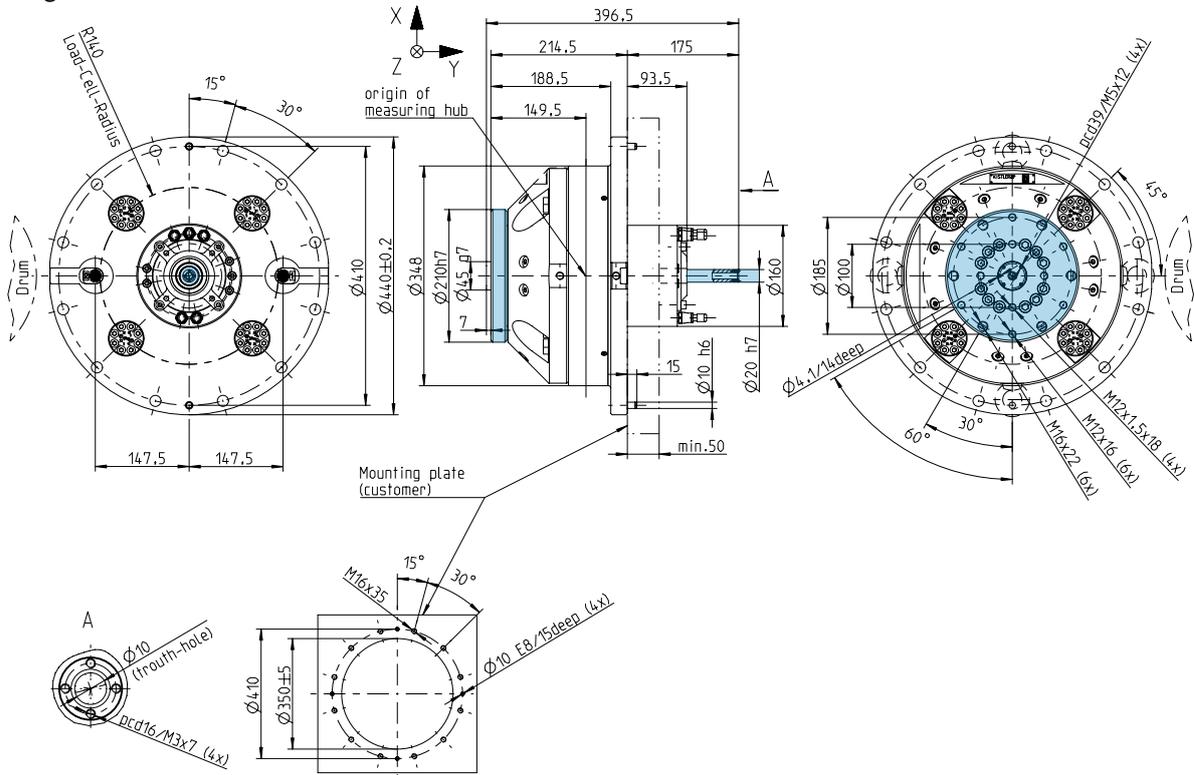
Übersichtszeichnung RoaDyn S260; rotierende Teile sind blau eingefärbt
